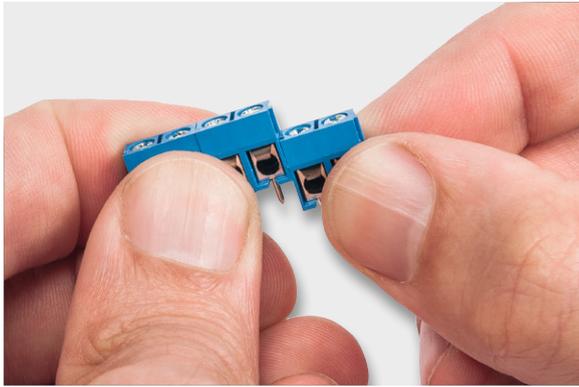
So werden die Schraubklemmen zu einem Block zusammengesetzt.
